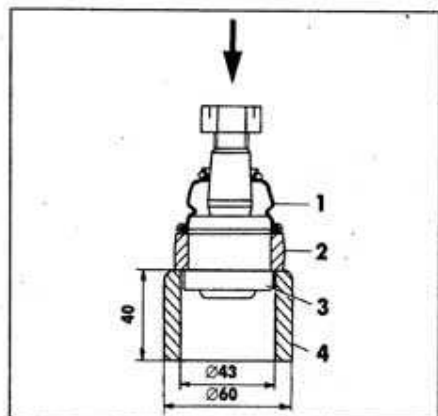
Выпрессовка шарнира рулевых тяг:
